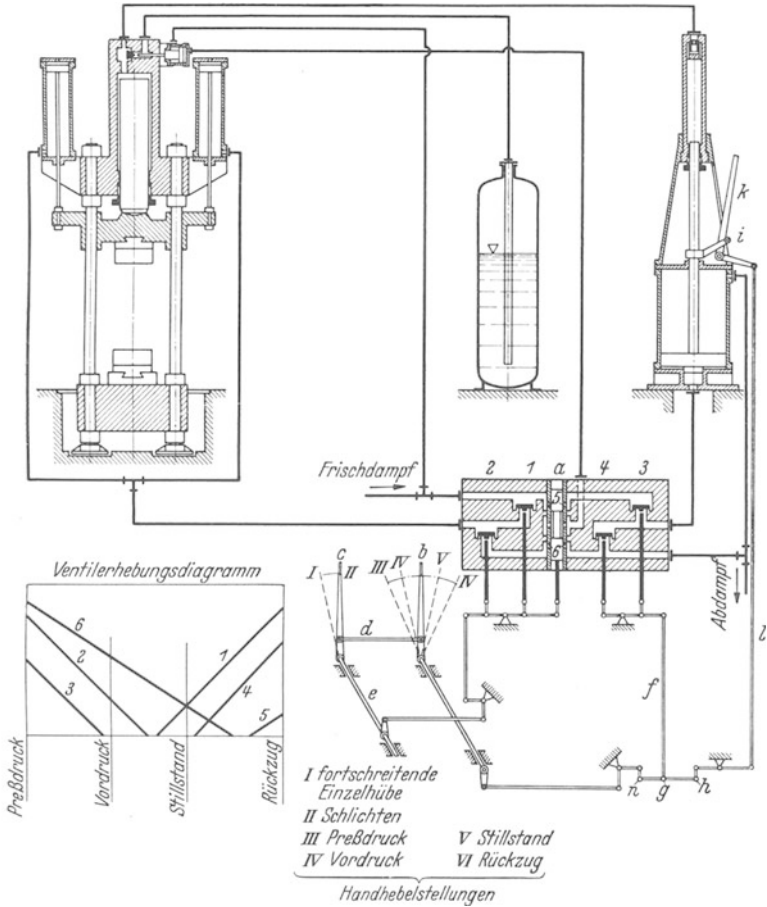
Steuerschema für eine dampf- oder lufthydraulische Einzylinder-Schmiedepresse.
